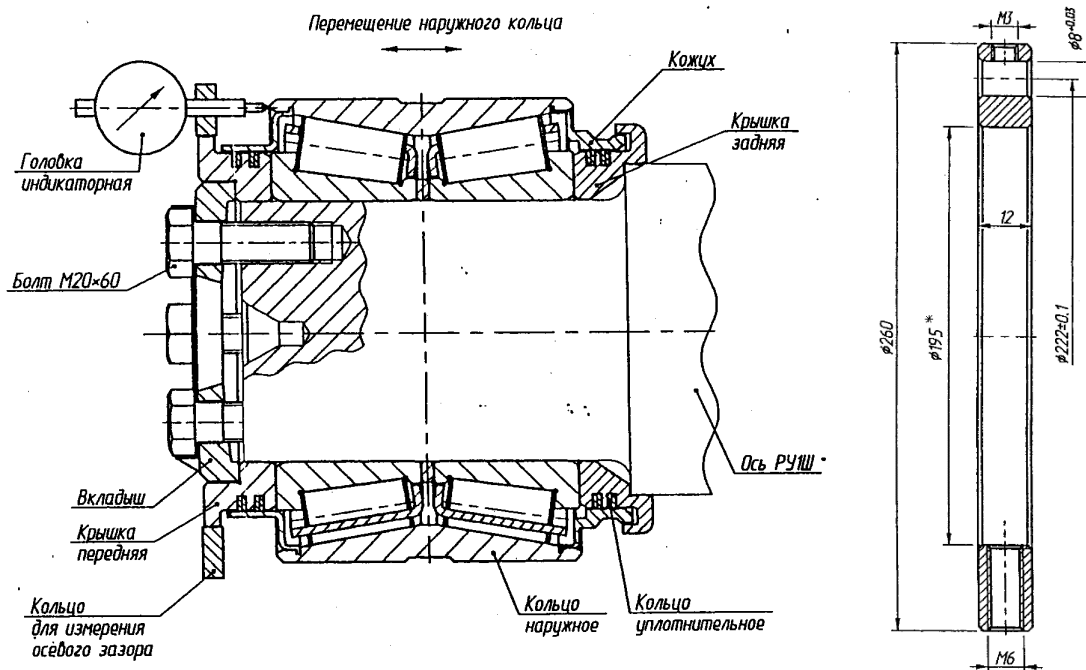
Схема измерения осевого зазора подшипника в габаритах 130x230x150 типа ТВУ 130 или «Вренсо» и кольцо для установки на фланец передней крышки или вкладыш подшипника (по отверстию диаметром 195*)
